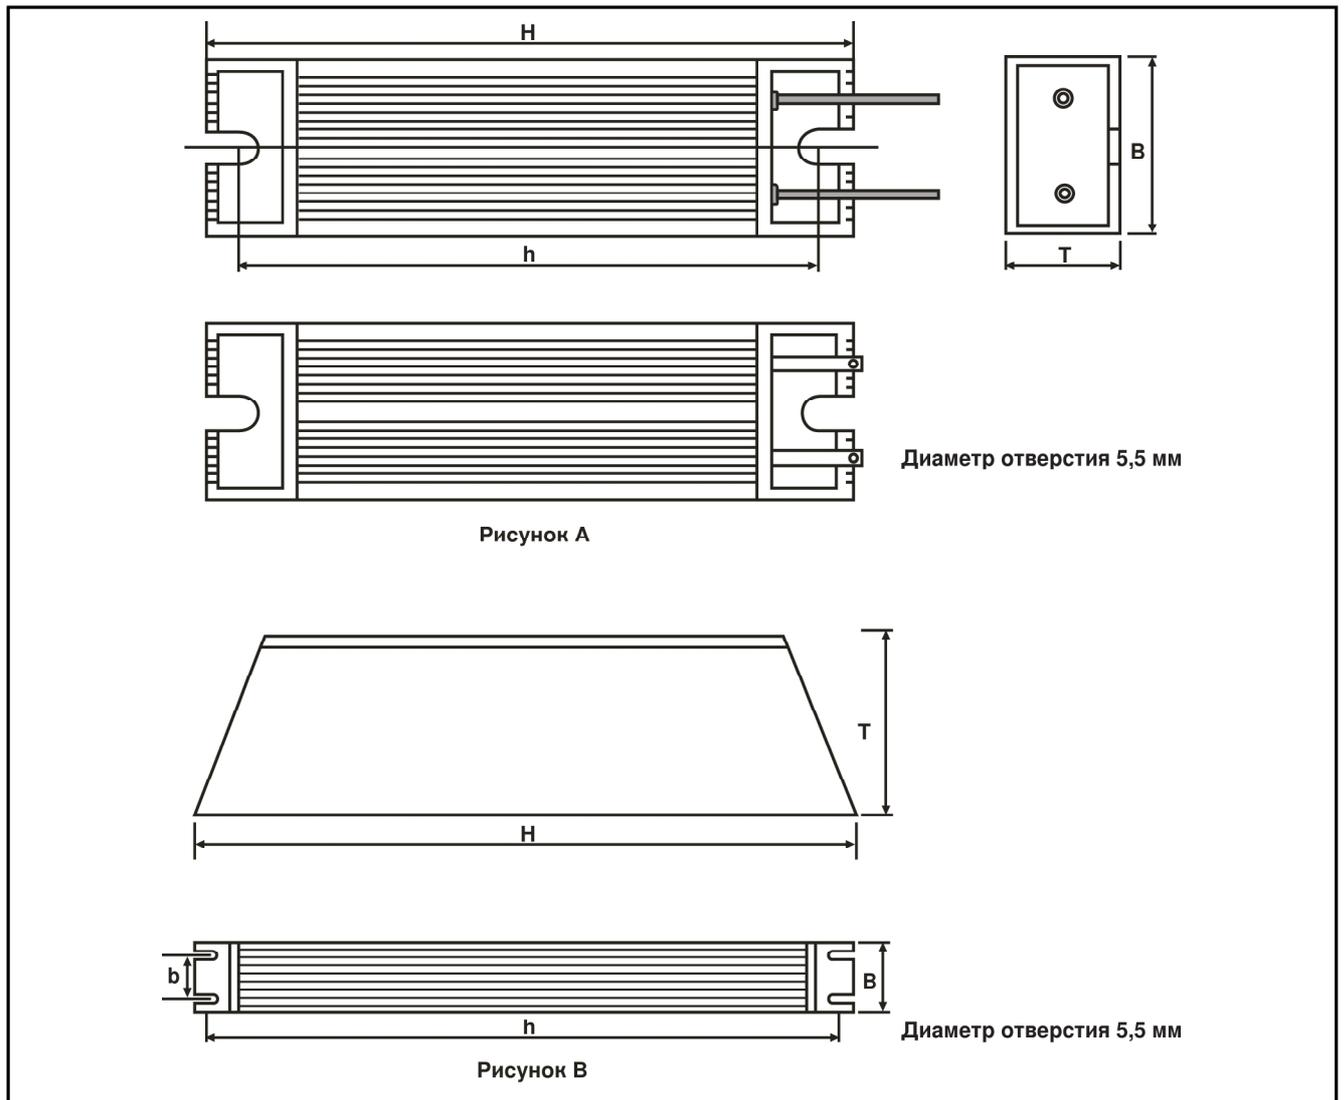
Тормозной резистор в алюминиевом корпусе
